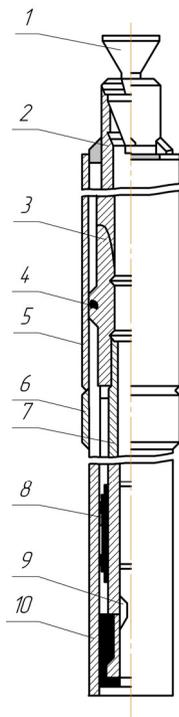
Резьбовой разъединитель: 1, 9 – верхняя и нижняя части секционной разъединительной пробки; 2 – переводник; 3 – nipple с левой резьбой; 4 – уплотнительная манжета; 5 – раструб; 6 – муфта с левой резьбой; 7 – несущая труба; 8 – пакерующий узел; 10 – обсадные трубы хвостовика
